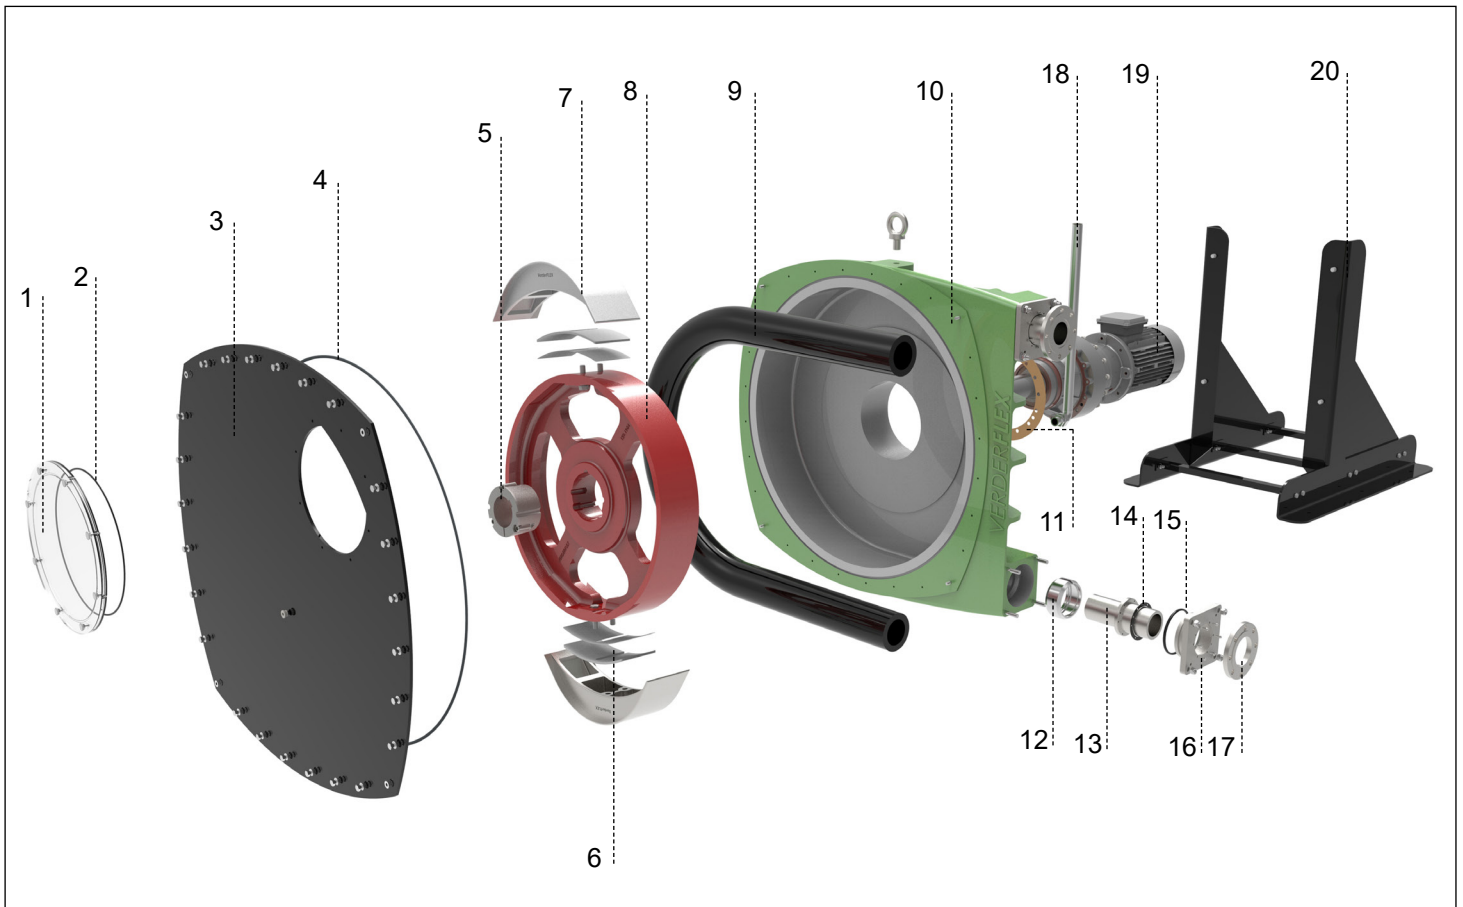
VF 100 Vue Éclatée (Vue Générique)
